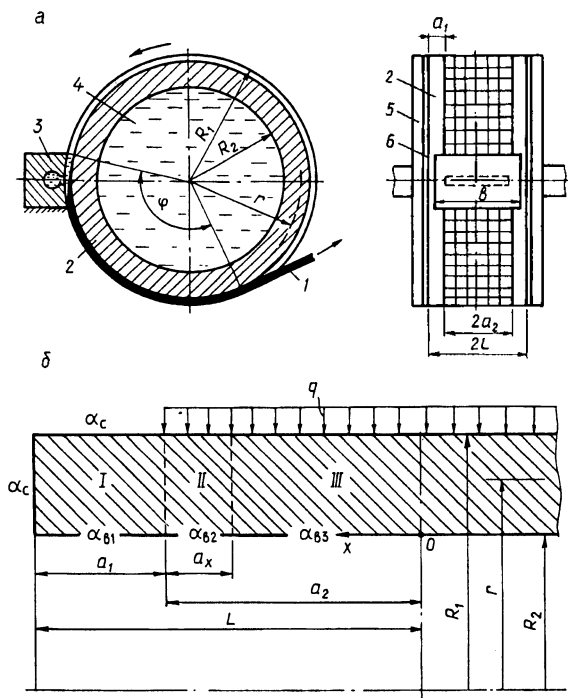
Схема к расчету температурного поля формообразующего валка при неравных условиях теплообмена на его водоохлаждаемой поверхности: а — схема литья решетчатой ленты (1 — отливка; 2 — формообразующий валок; 3 — башмак; 4 — вода; 5 — крышка; б — прокладка); б — схема теплообмена валка с отливкой водой и воздухом: I, II, III — зоны
